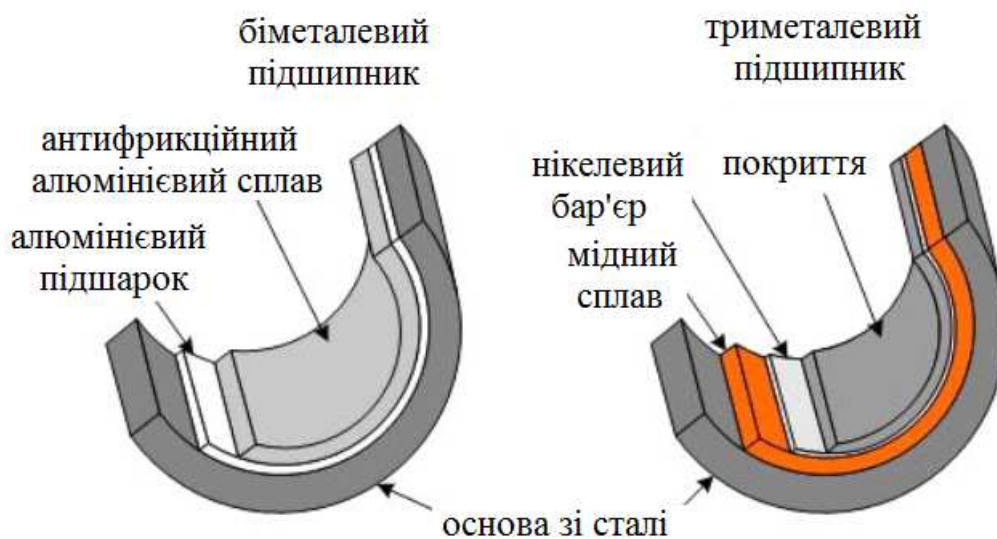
Бі - та три металеві підшипники ковзання
